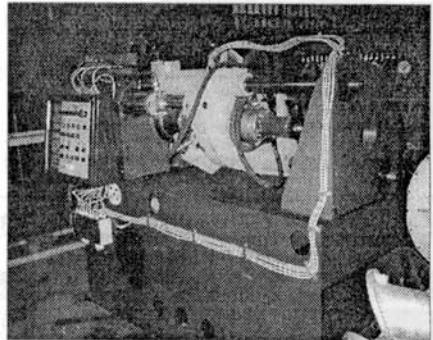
Машина СТ-120 для конвенционной сварки трением
